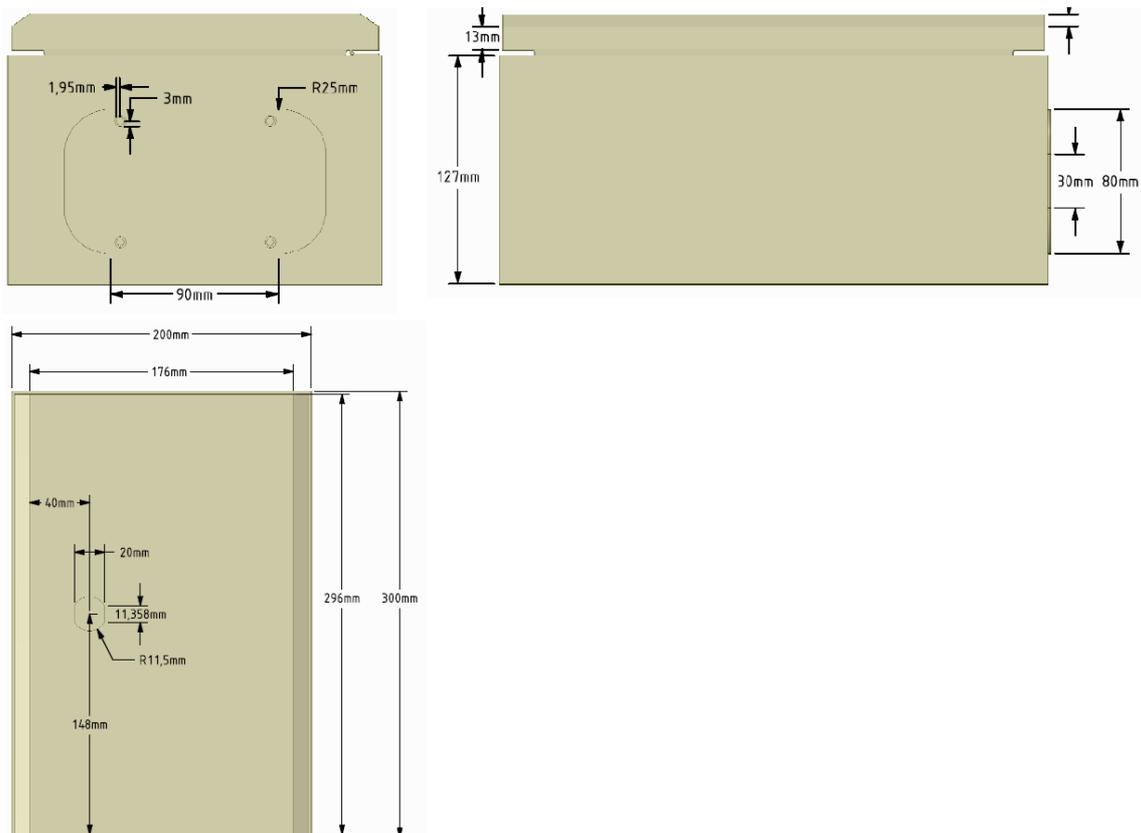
Dimensiones en alzado, planta y perfil izquierdo de la caja envolvente.
